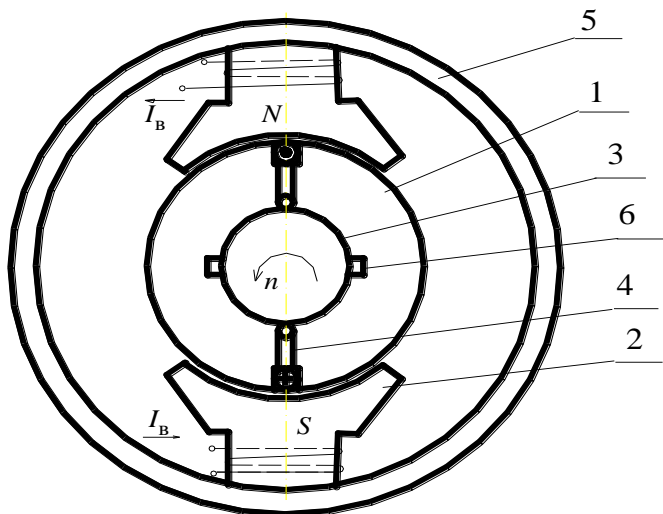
Эскиз конструкции машины постоянного тока: 1- якорь; 2- главный полюс; 3- коллектор; 4- соединение обмотки якоря с коллектором; 5- станина; 6- щетка
